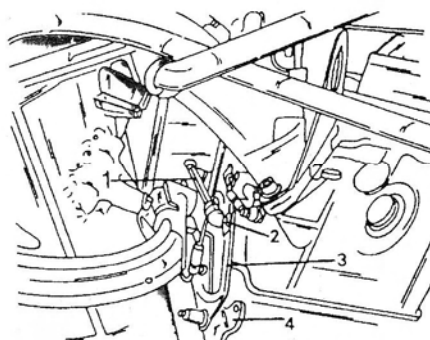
Регулировка привода дроссельной заслонки на автомобиле с обычной коробкой передач.
